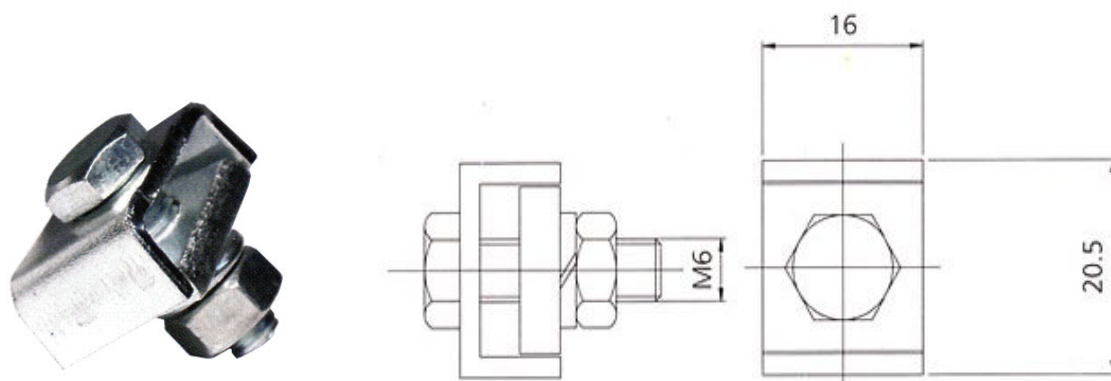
Общий вид стыковочного зажима для коробов с предустановленными медными полосами.
